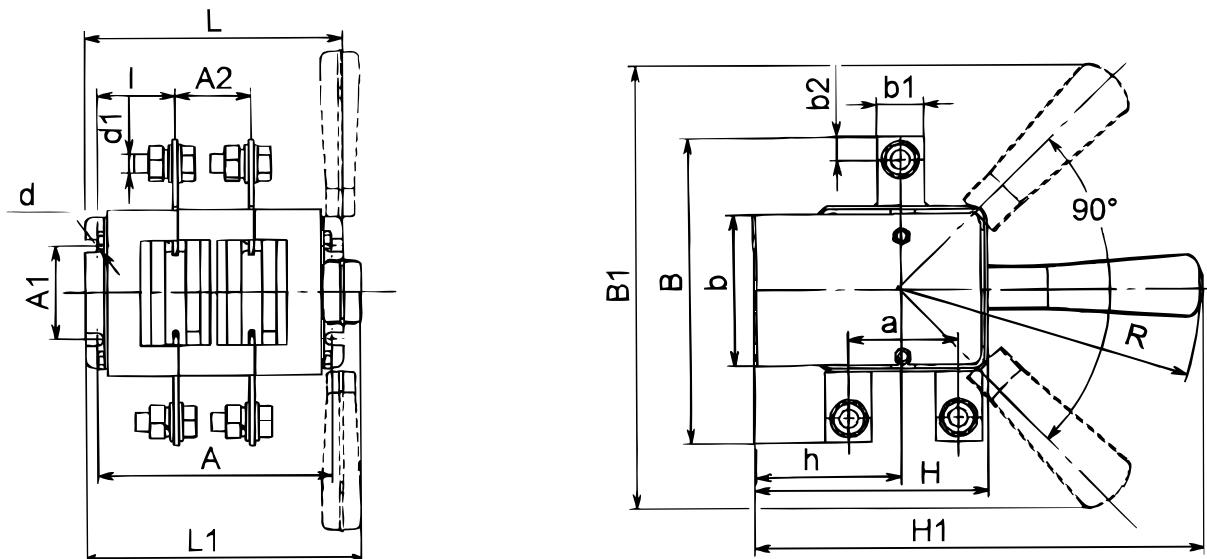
Выключатель-разъединитель на два направления двухполюсный с боковой рукояткой
